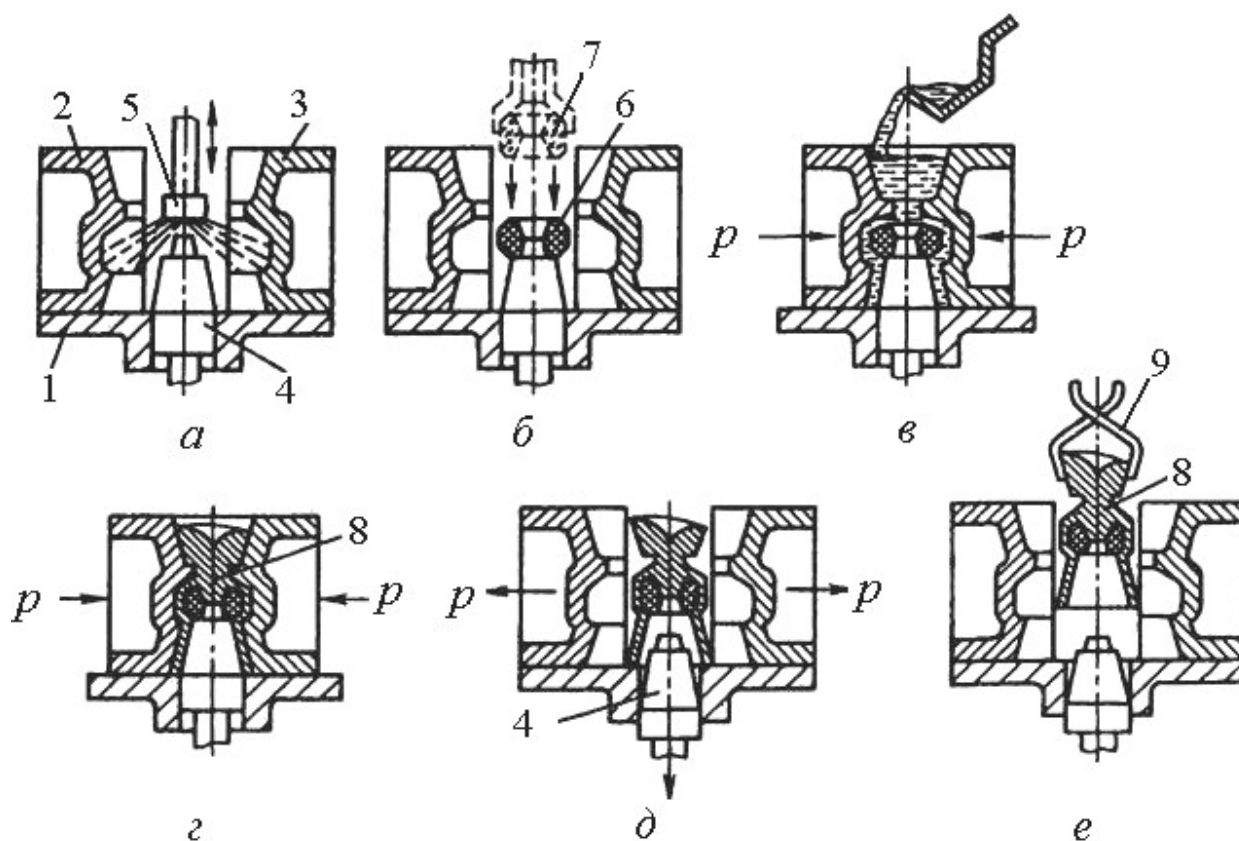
Последовательность операций изготовления отливок в кокиль: 1 – поддон; 2, 3 – симметричные полуформы; 4 – металлический стержень; 5 – pulverизатор; 6 – песчаный стержень; 7 – манипулятор; 8 – отливка; 9 – спецприспособление
